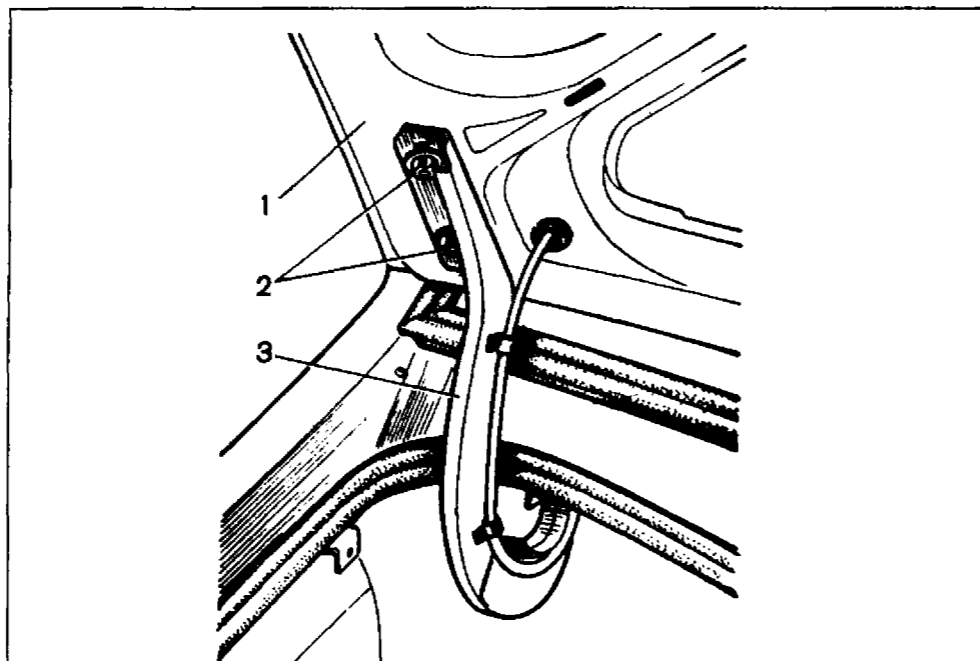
Снятие крышки багажника: 1 — крышка багажника; 2 — гайки крепления крышки багажника; 3 — подвижное звено петли
